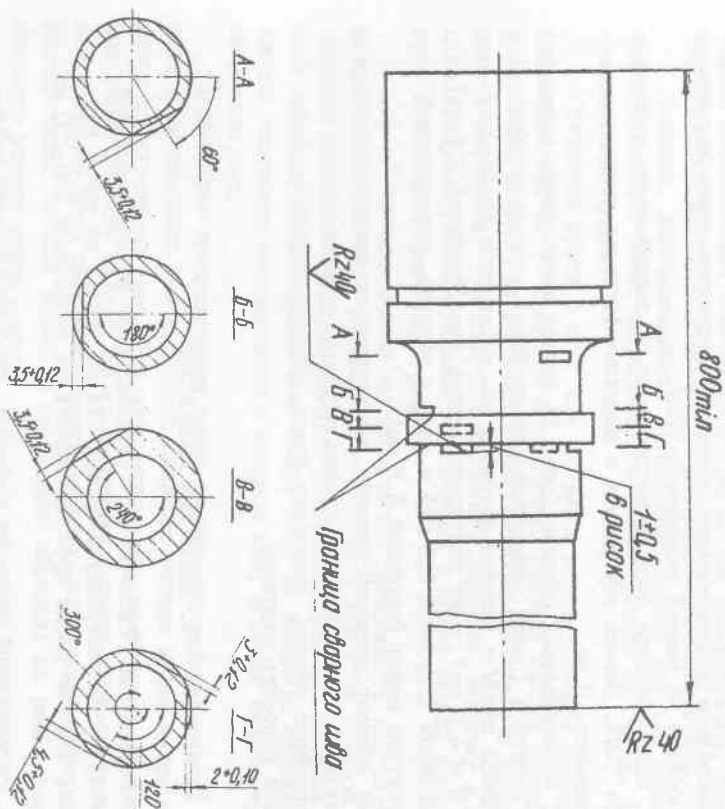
Испытательный образец для настройки дефектоскопа при контроле зоны сварного шва трубы ТБПБ
